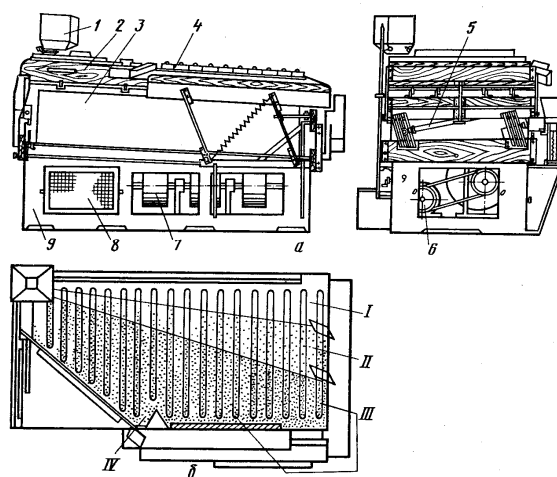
Пневмосортировальний стіл БПС: а – загальний вид: 1 – живильний пристрій; 2 – вібростіл; 3 – повітряна камера; 4 – лотки для збору і висновку фракцій; 5 – шатун; 6 – привод з варіатором; 7 – вентилятор; 8 – повітряний фільтр; 9 – станина; б – схема поділу зерна на деку столу: I – легкі відходи; II – проміжна фракція; III – очищене зерно; IV – важкі відходи.
